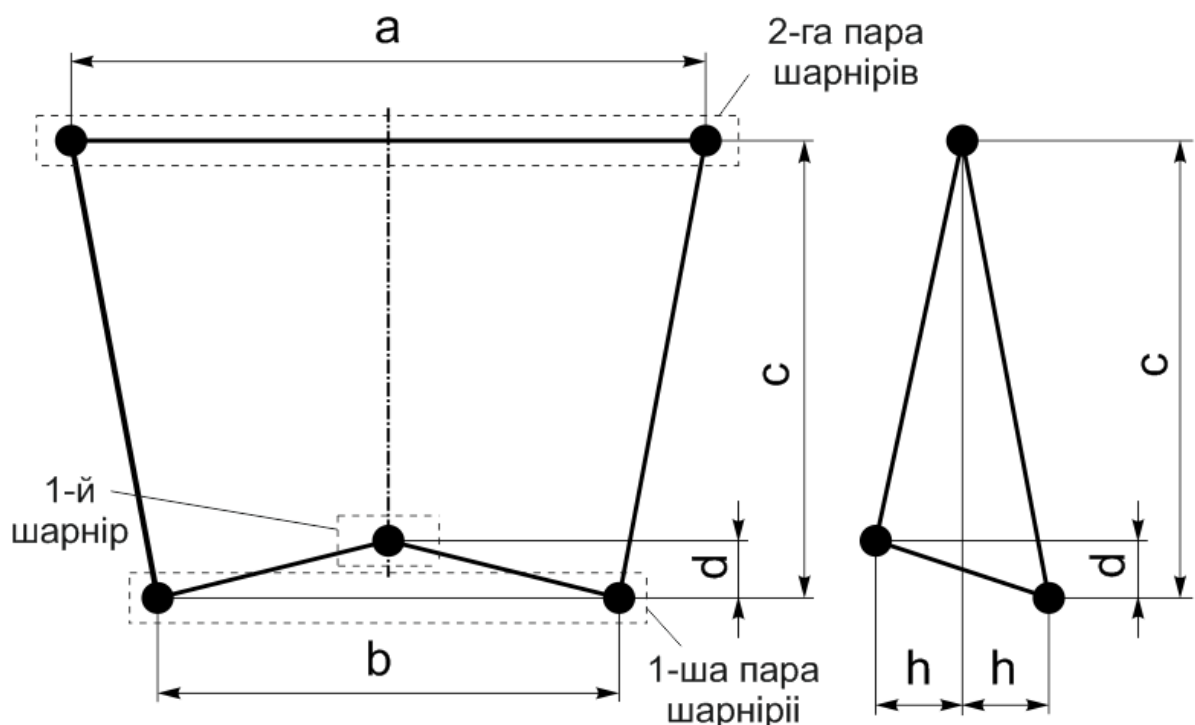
Схема з основними розмірами конструкцій верстата
